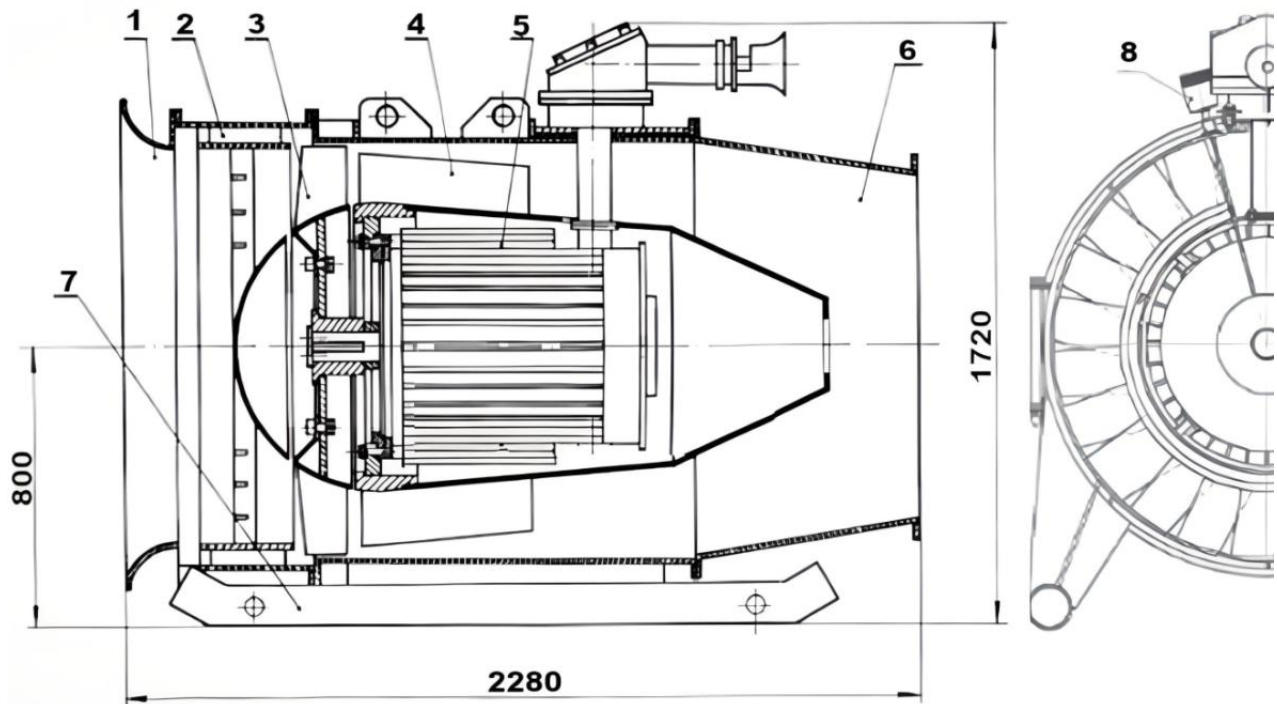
Вентилятор ВМЭ-12А: 1 – входной коллектор; 2 – противосрывное устройство с коком и защитной решеткой; 3 – рабочее колесо; 4 – корпус вентилятора со спрямляющим аппаратом; 5 – взрывобезопасный электродвигатель; 6 – конусный переходной патрубок; 7 – салазки; 8 – тавотница
